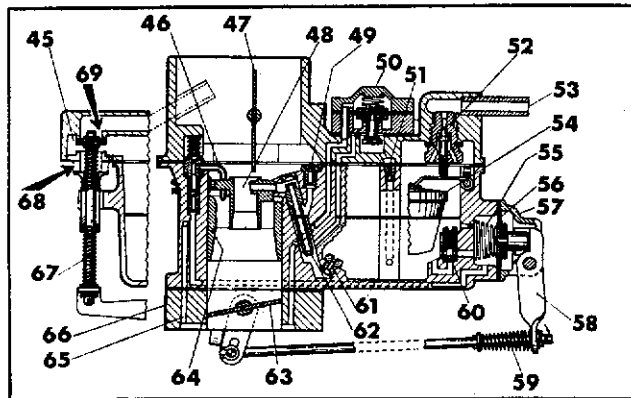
Coupes du carburateur Solex 32/32 DIDTA
